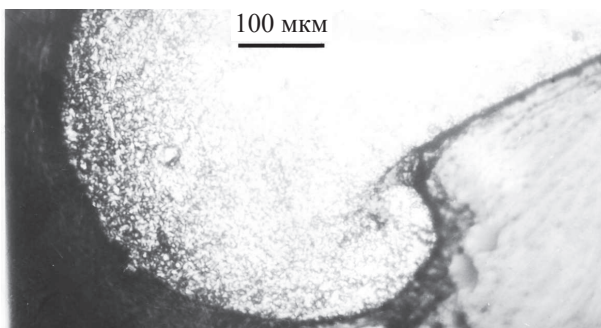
Сечение режущего клина с деформацией режущей кромки резца твердостью HRC = 45
